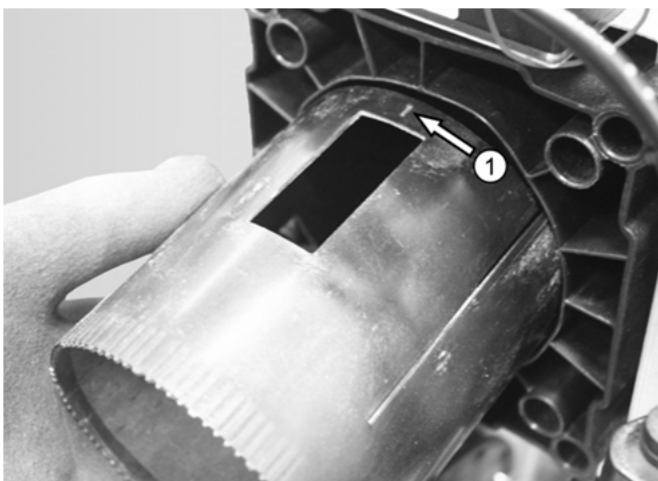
Einführung der Luftdrossel in das Gehäuse (Beispiel: Segmentnummer I)
